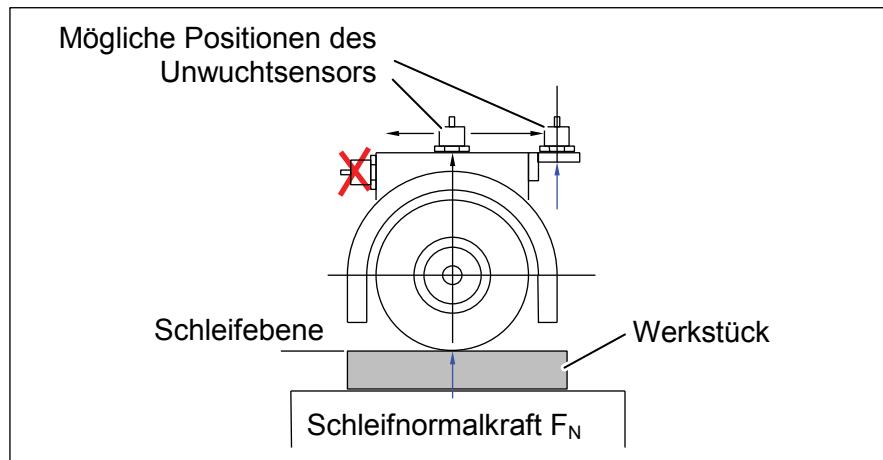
Unwuchtsensor an einer Flachschleifmaschine
